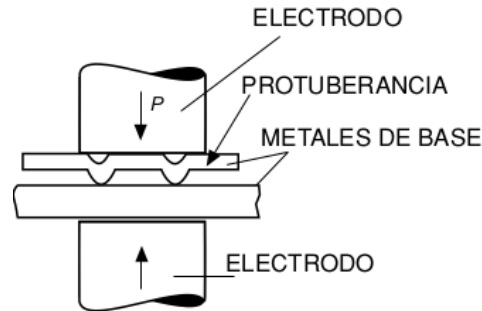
Detalle del proceso de soldadura por protuberancias. Fotografía obtenida de la web GasolSRL.com
